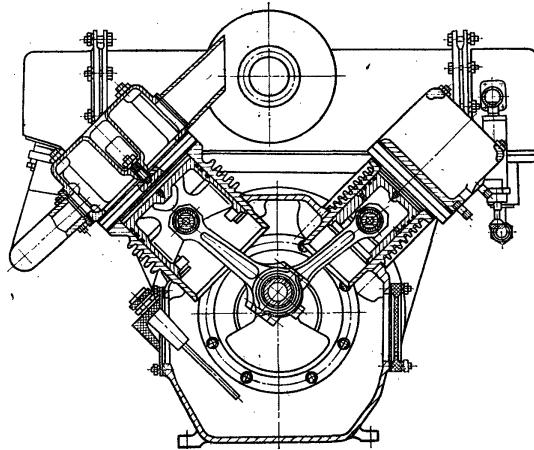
Поршневой V-образный двухцилиндровый бескрайцкопфный компрессор с воздушным охлаждением
